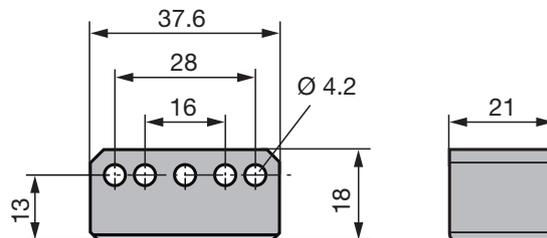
Medidas de montaje del sensor de posición BTL6-A-3801-2
